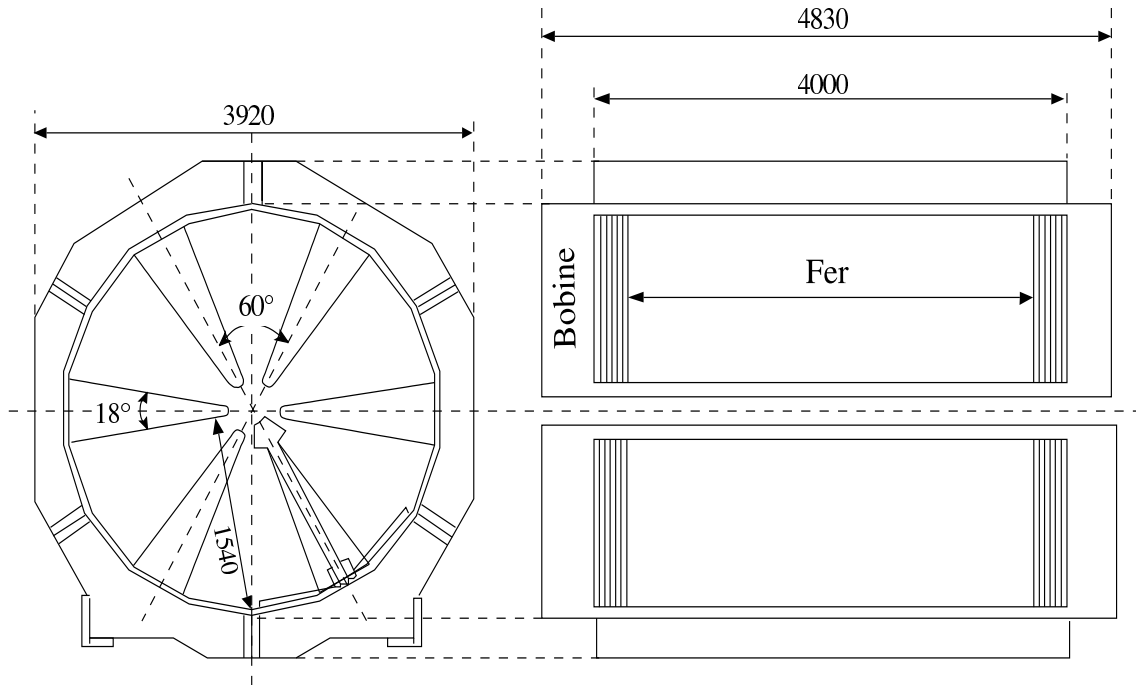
Vue de face et vue de côté de l'aimant toroïdal (ACM).
